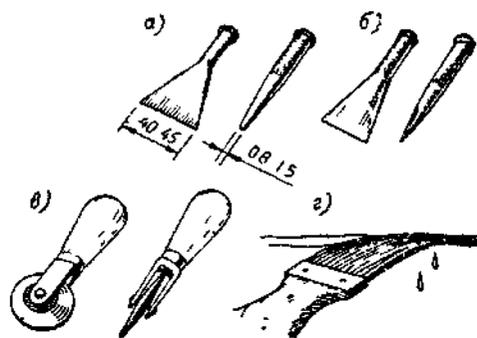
Инструмент для конопатки: а — лебеда для конопатки; б — лебеда для разладки пазов; в — диск для конопатки тонкой обшивки; г — окраска паза флейцем.
